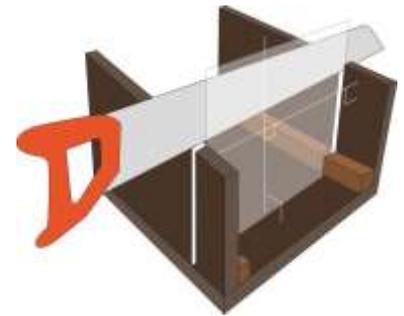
exemple boîte de découpe à dimension pour panneaux HYBRIS
